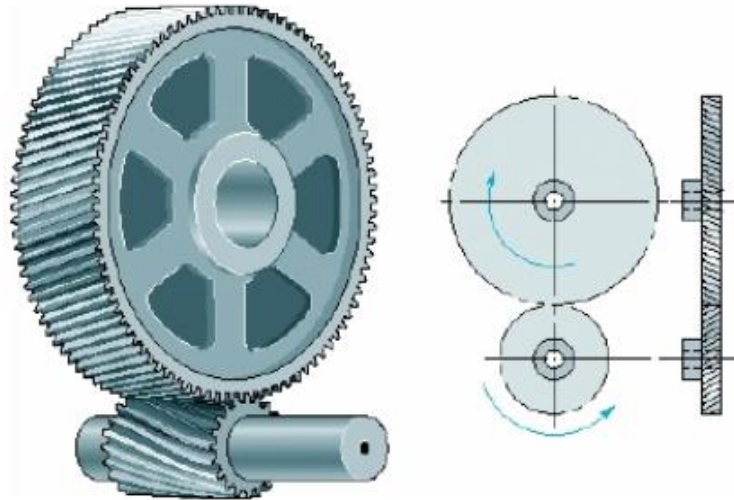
Engrenagens cilíndricas de dentes helicoidais [15]
